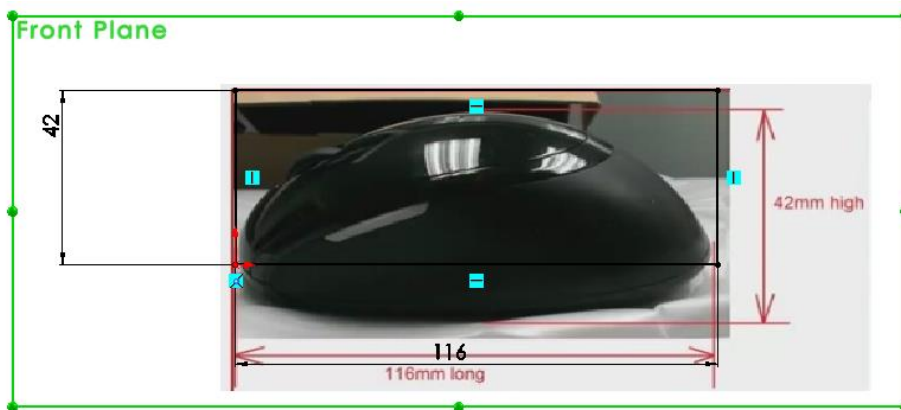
Imaginea importată și aliniată în dreptunghiul desenat în planul Frontal
